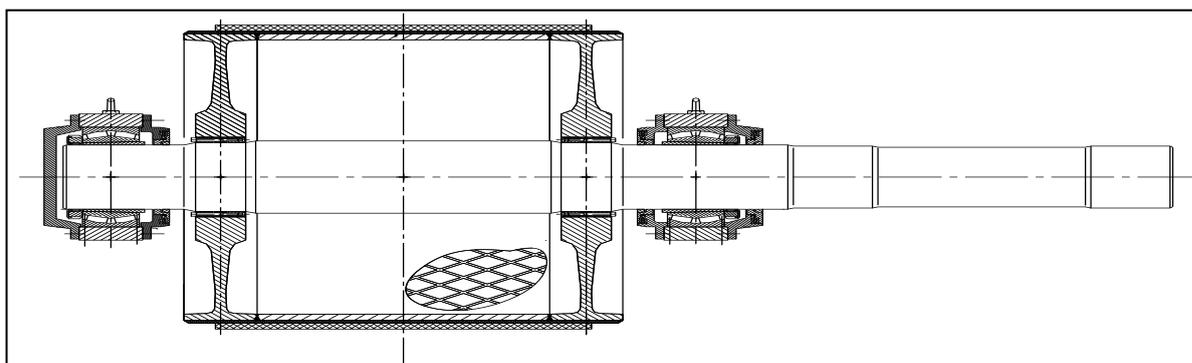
Типовой ведущий шкив для одного узла привода
